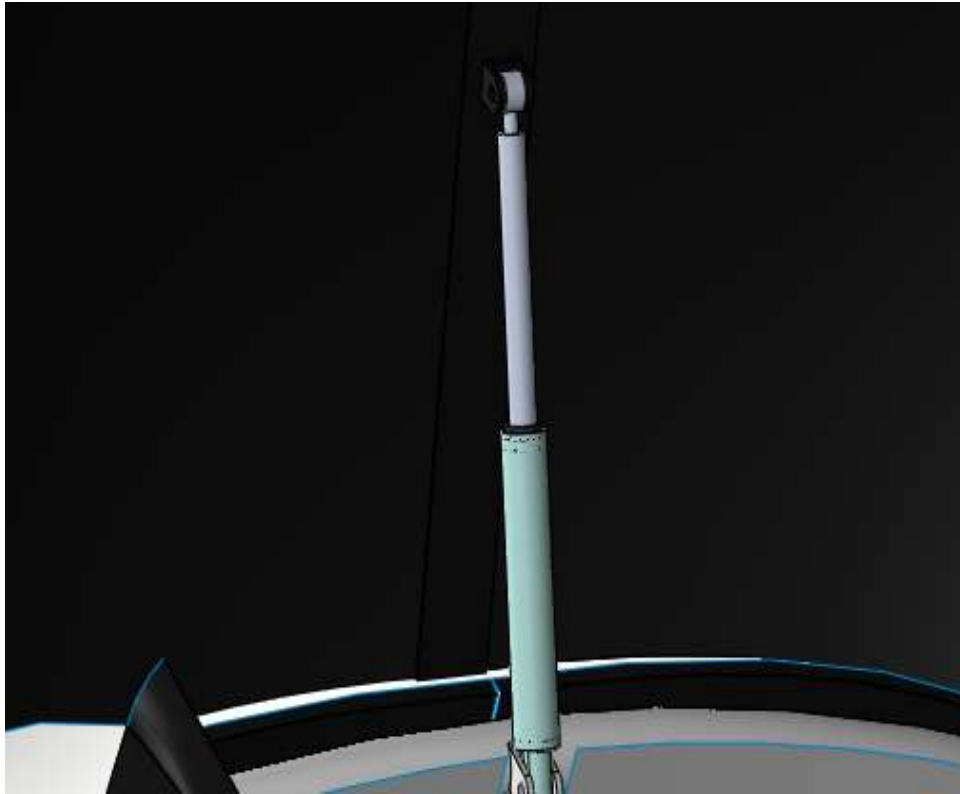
Sistema de apertura de puerta superior con pistón de elevación. Fuente: (Vaca, José, 2018)
